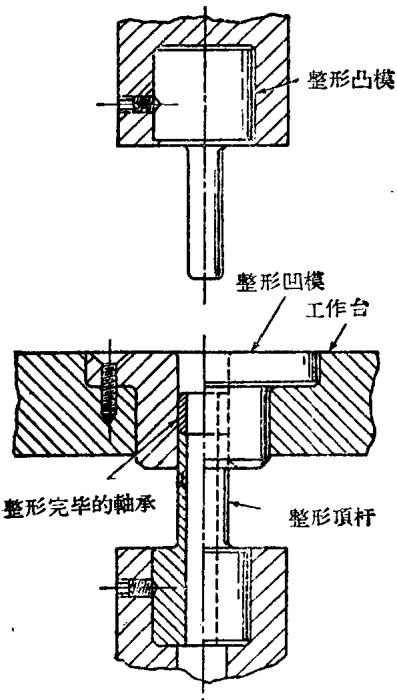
当單純的压制和燒結不能取得某些尺寸公差时，通常即在燒結后进行整形。图中即为用于一个需要精密的外徑与孔徑尺寸的圓筒状工件的模具。由上凸模貼紧工件的内孔将工件压入外徑整形凹模中，当工件停止在下方的頂杆面上时，凸模繼續压进而完成內孔的整形。然后抽除凸模，待下方頂杆上升到工作台平面而頂出工件。
